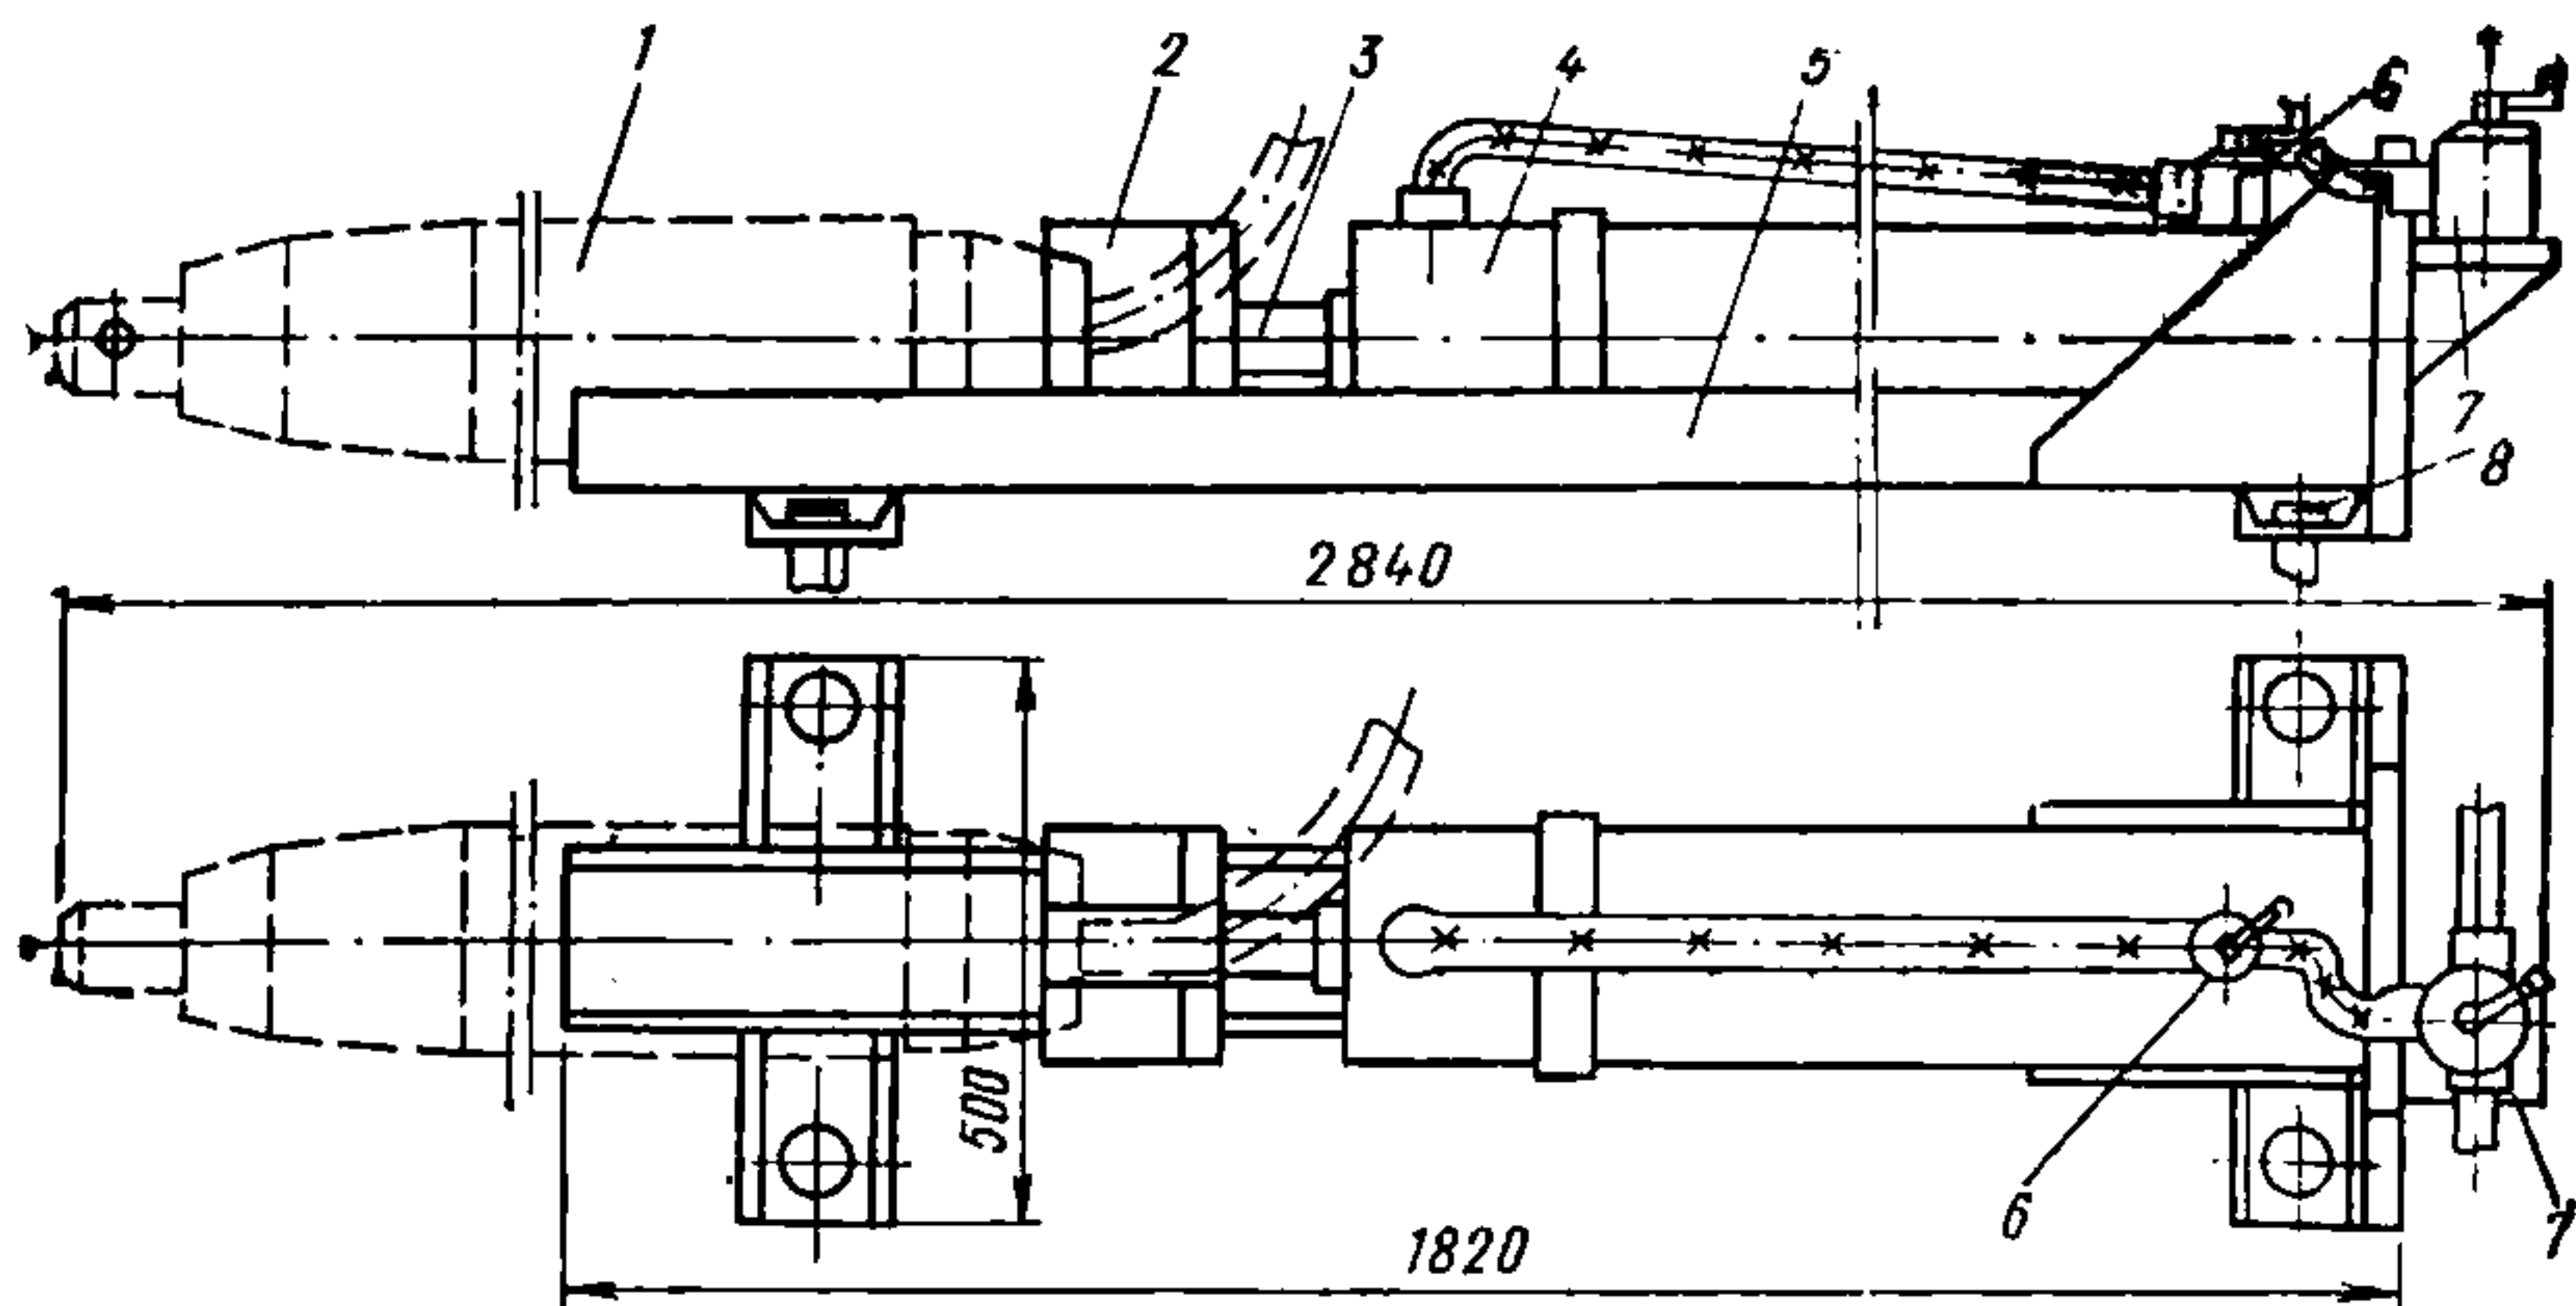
Схема стартового устройства для пневмопробойника СО-134 (ПР-400)
